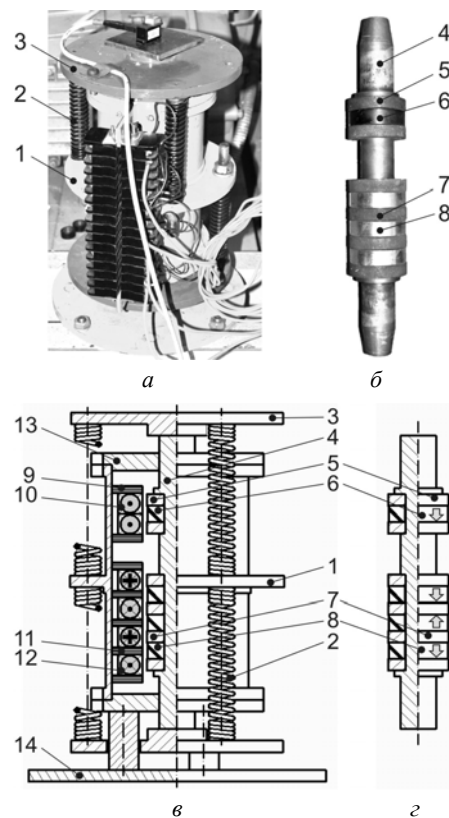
Коаксиально-линейный двигатель с магнитной пружиной: а – внешний вид КЛД-МП; б – внешний вид бегуна КЛД-МП; в – конструкция КЛД-МП; г – конструкция бегуна КЛД-МП
